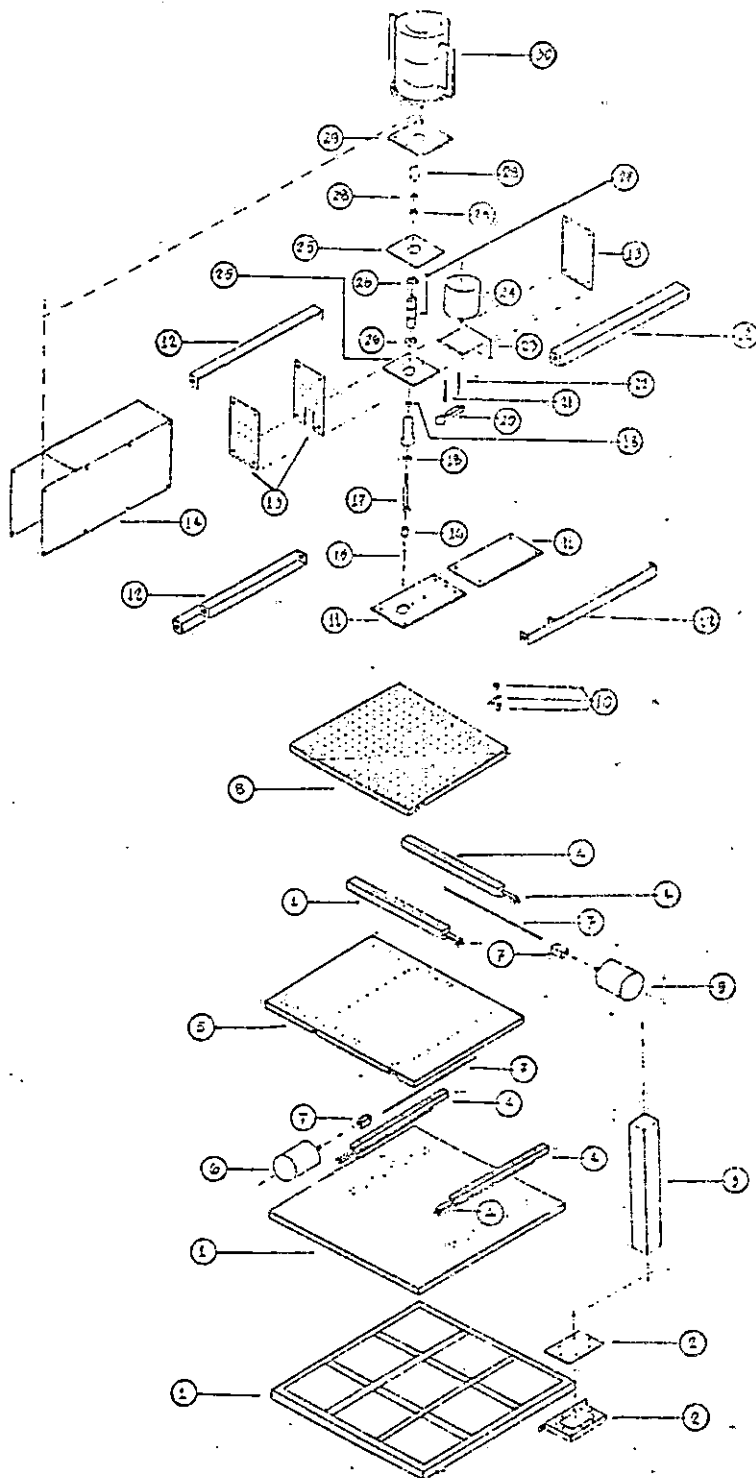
Partes que componen la máquina perforadora CNC-EIE
